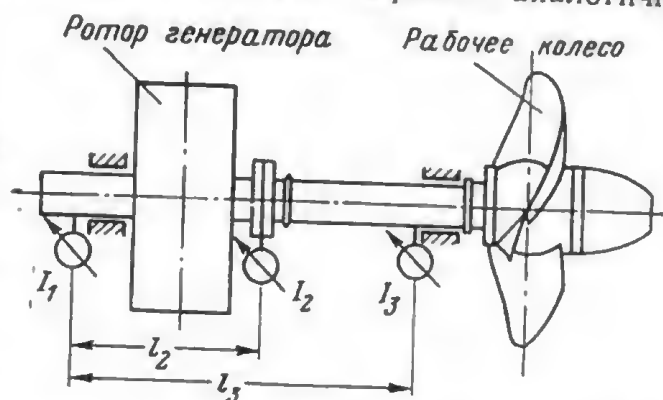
Схема проверки общей линии вала капсульного гидроагрегата с раздельными валами.
